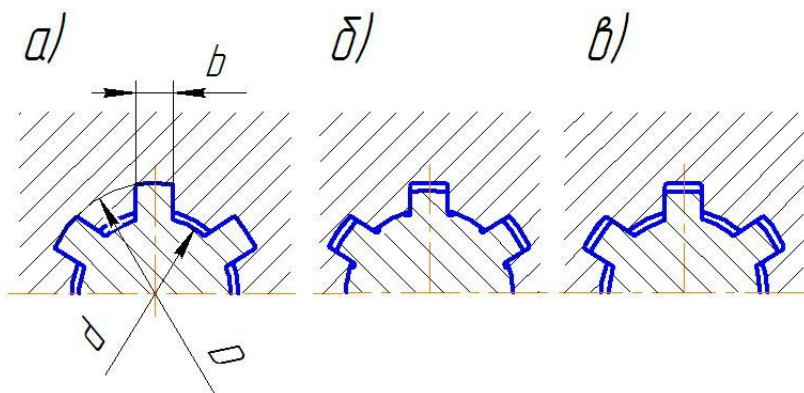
Конструкция и способы центрирования прямобоочных шлицевых соединений
